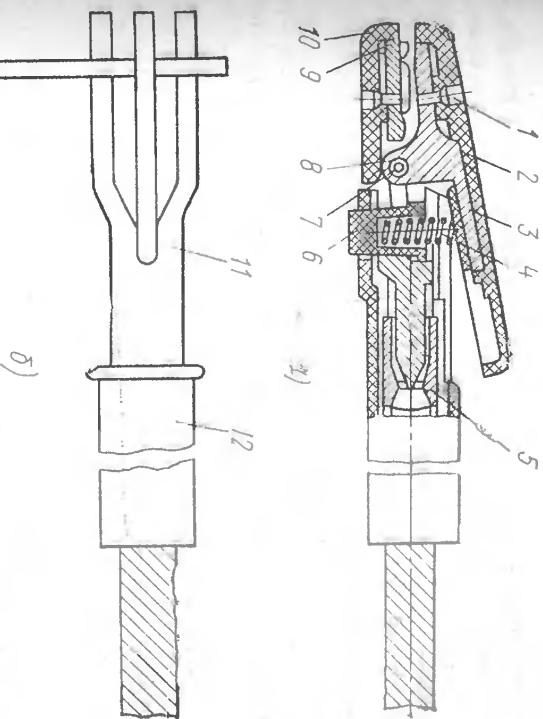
Электрододержатели для ручной дуговой сварки:
